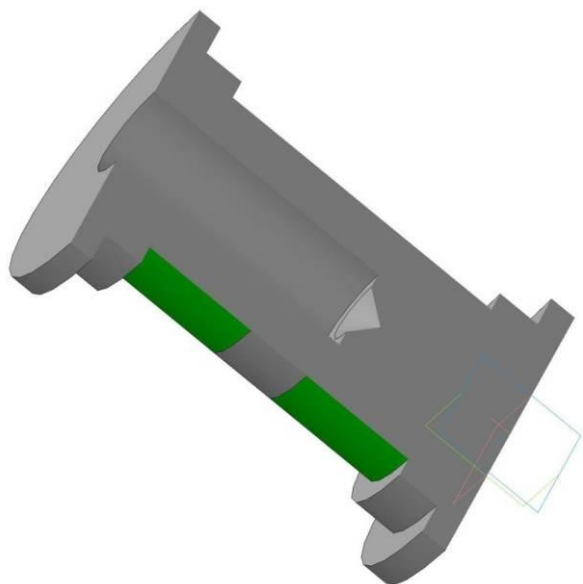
3D-модель части бурового вала с фланцевыми элементами предварительного закрепления и поверхностями трения
